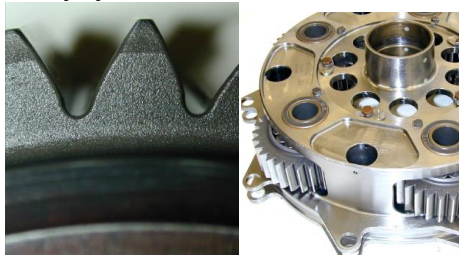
Асиметричні зубці евольвентного колеса та блок коліс з асиметричними зубцями планетарного редуктора гелікоптера
